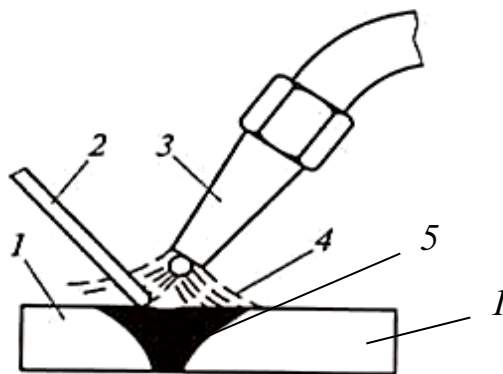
Схема газовой сварки: 1 – заготовки; 2 - присадочный материал; 3 – газовая горелка; 4 – газовое пламя; 5 – сварочная ванна
